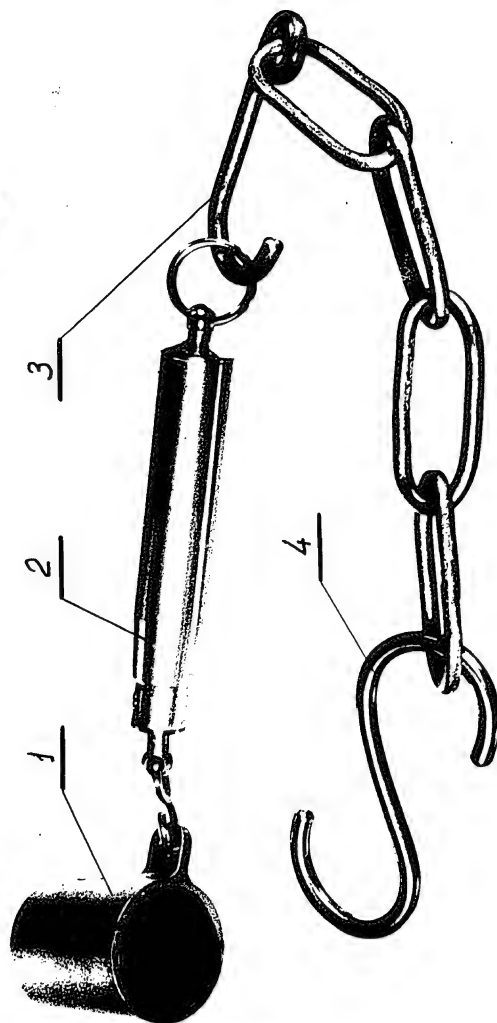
Припособление для замера усилий на рукоятке штурвала.
